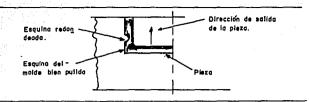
Recomendaciones para el diseño de entalladuras. (Ref. 8).
